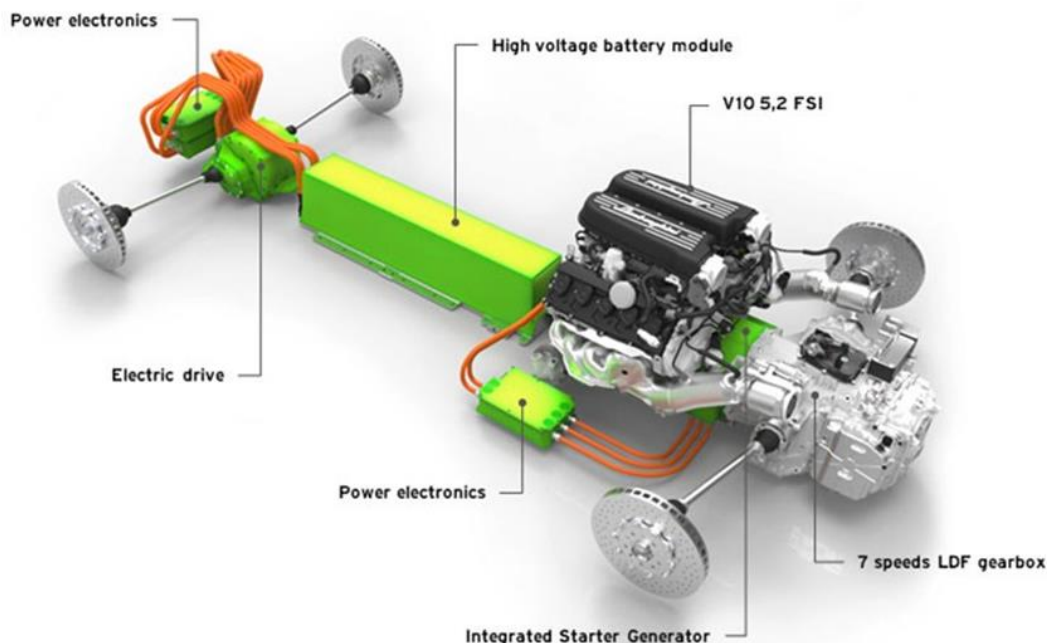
Vizualizace pohonu u Audi TT - hybrid [65]
